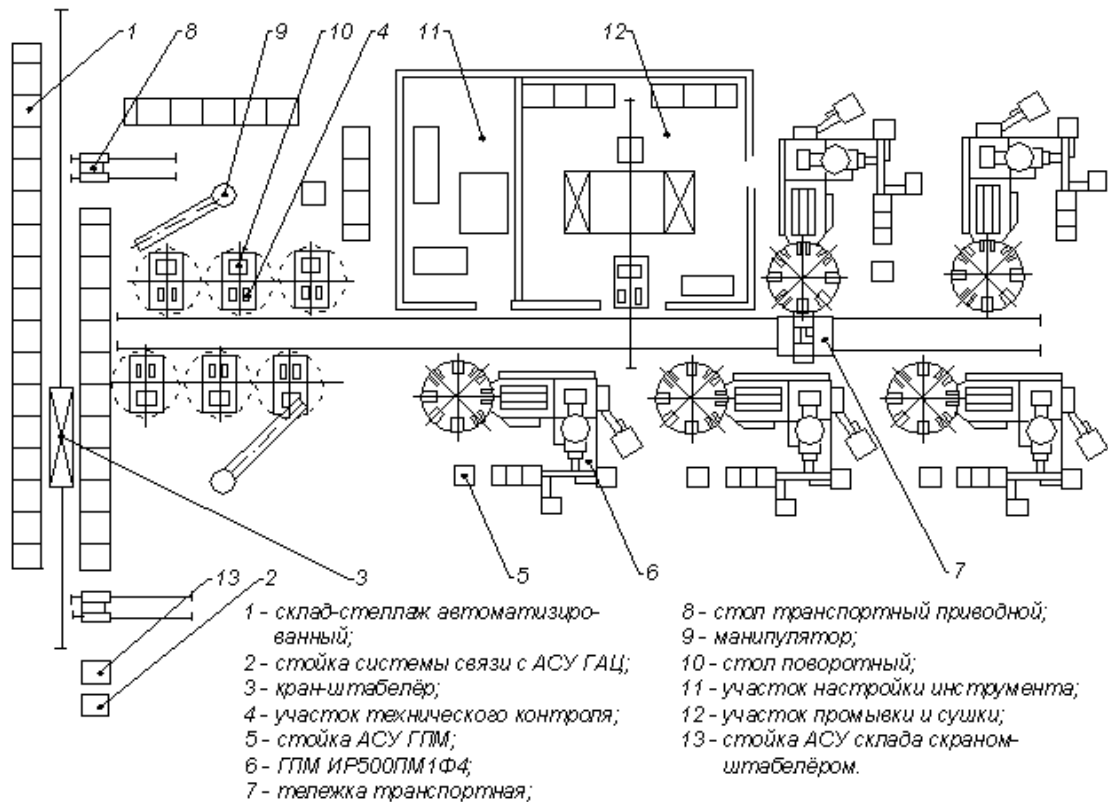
ГАУ с АТСС линейного типа, с поперечным расположением оборудования и рельсовой транспортной тележкой
